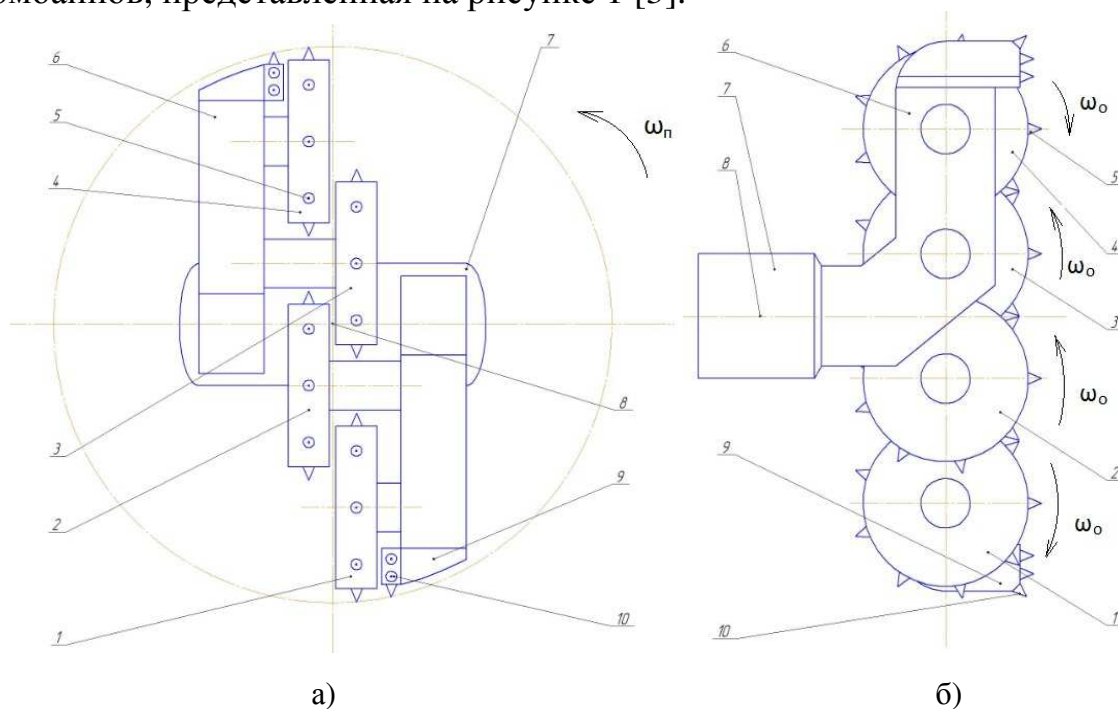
Схема исполнительного органа: а – вид спереди; б – вид сбоку
